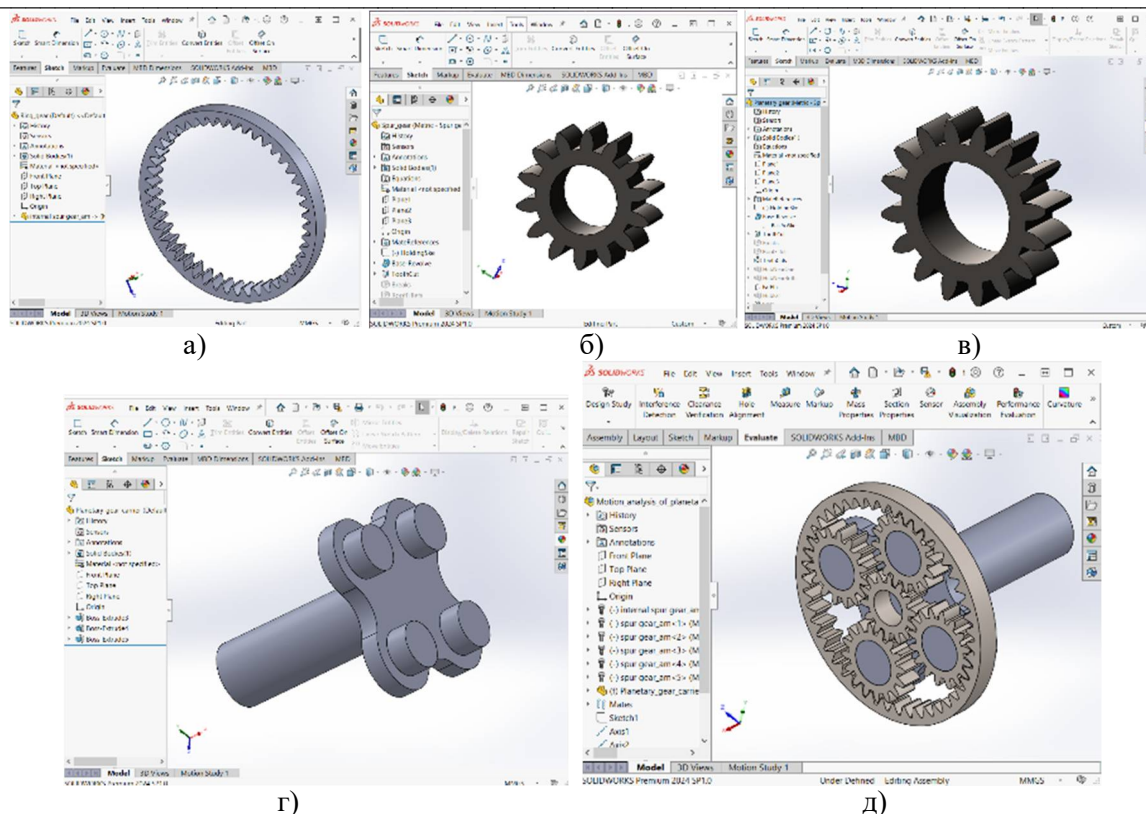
Загальний вигляд деталей планетарного редуктора: а) – вінцева (коронна) шестерня, б) – сонячна (центрально) шестерня, в) – планетарна шестерня, г) – водило, д) - збірка редуктора
